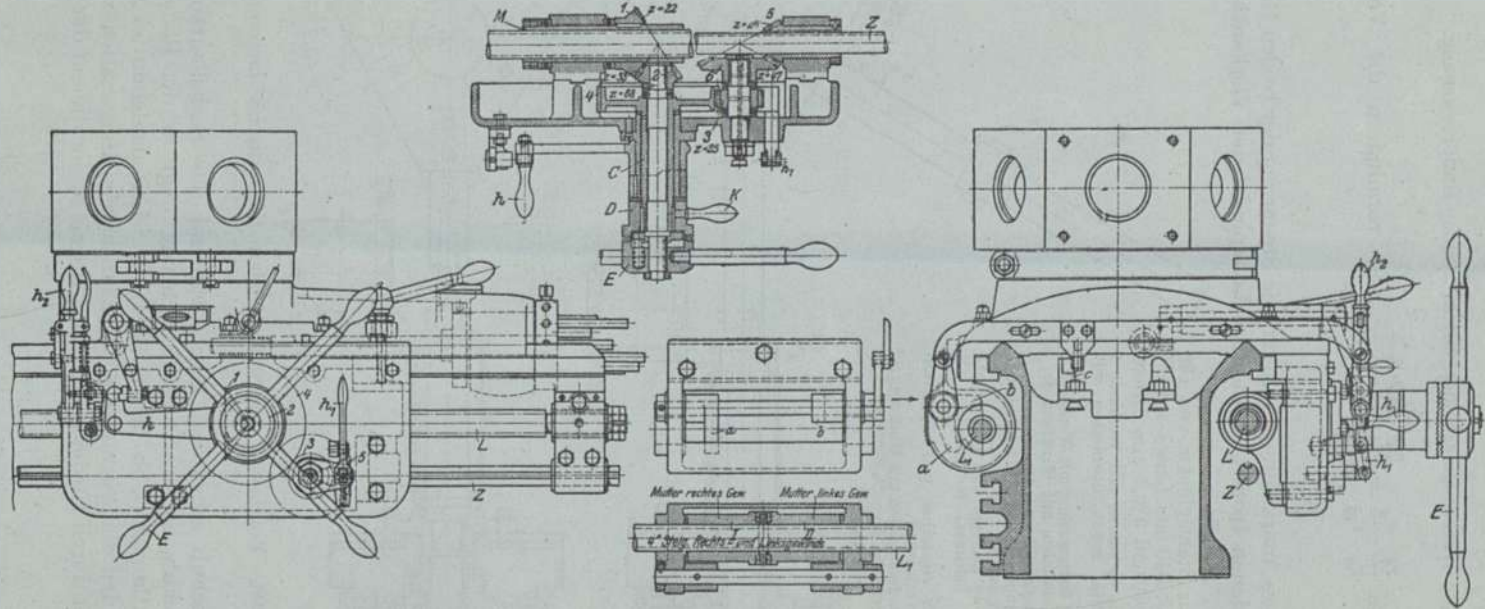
bis 294. Böhlinger-Revolverwerkzeugschlitten mit Schloßplatte.
